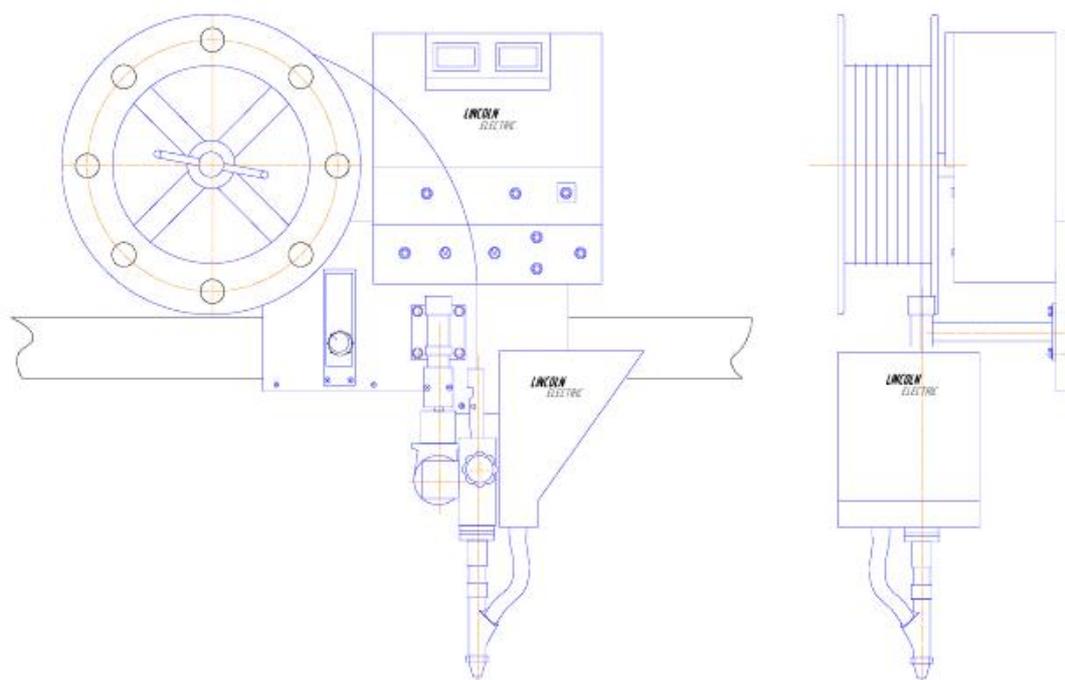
Сварочная головка NA-5 Lincoln Electric
